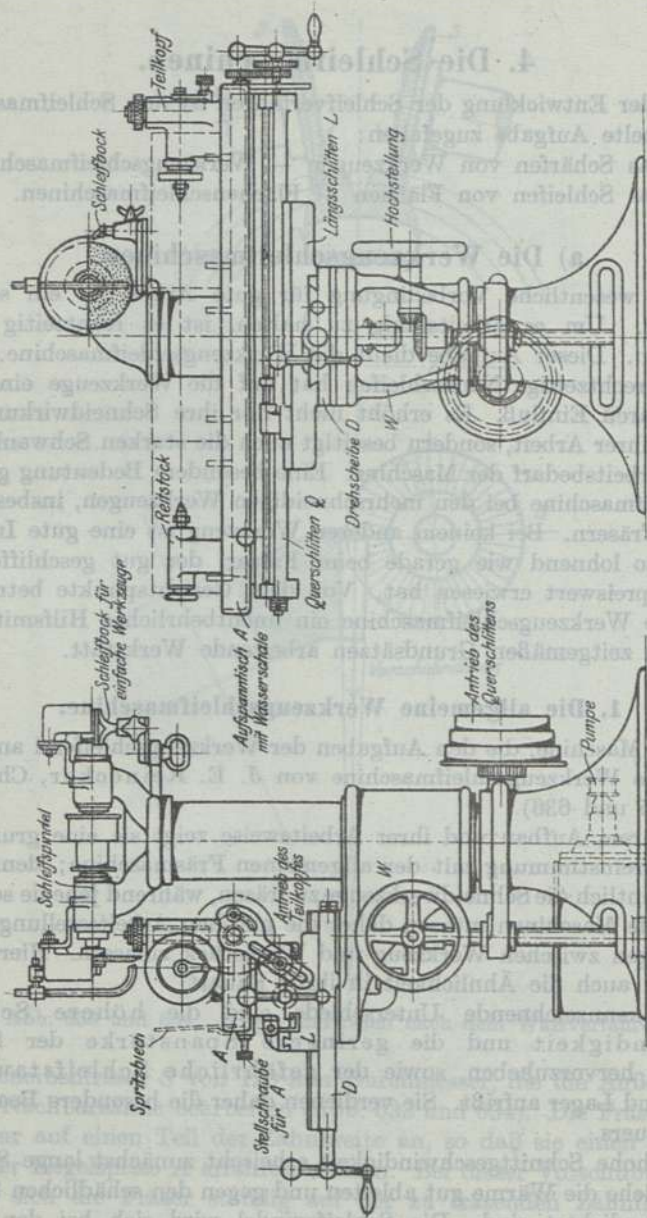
und 636. Werkzeugschleifmaschine J. E. Reinecker, A. G., Chemnitz.
